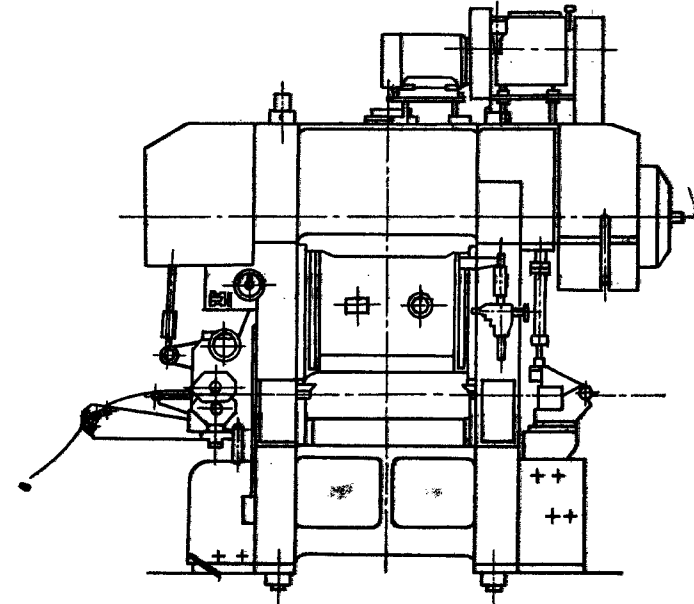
Быстроходный пресс с верхним приводом для твердосплавных штампов
